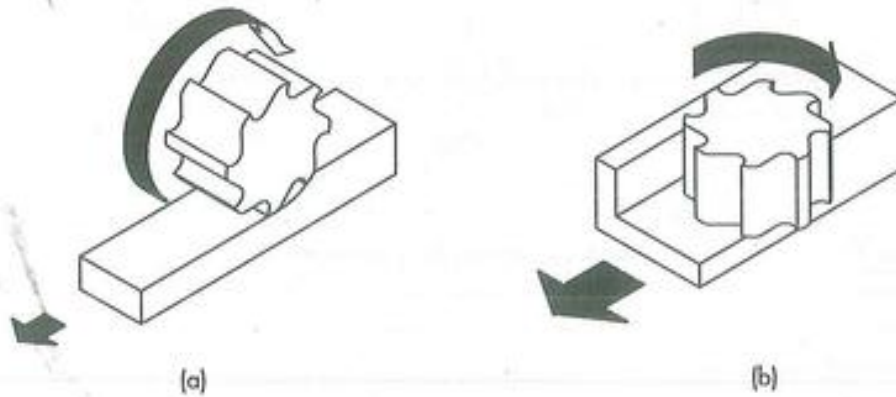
(a) Fresado cilíndrico. (b) Fresado frontal.
